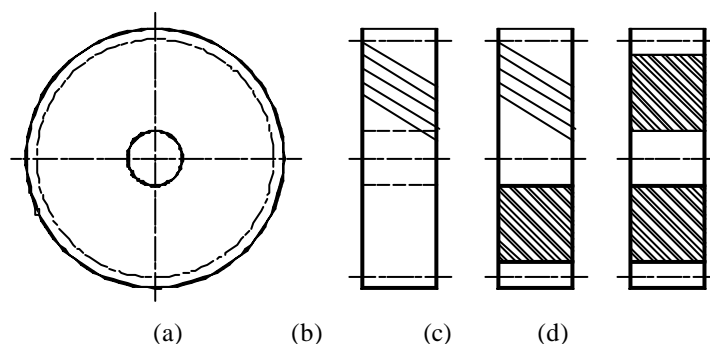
Engrenagem cilíndrica de dentes helicoidais
